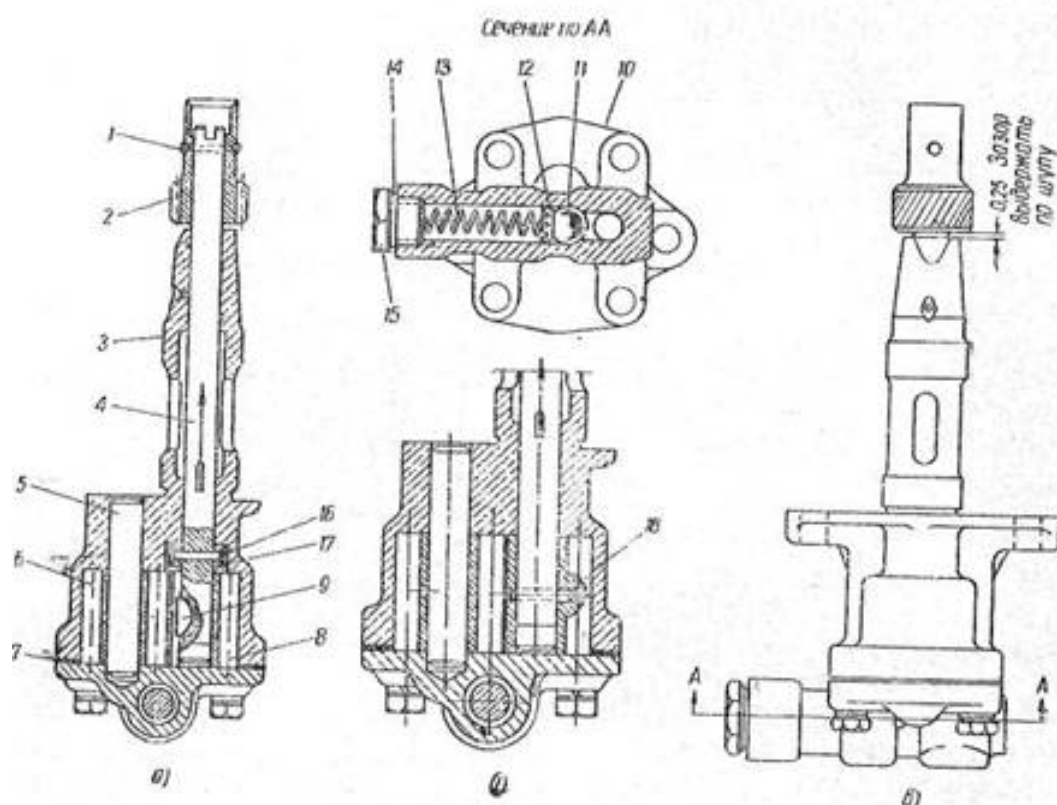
Масляный насос двигателей ГАЗ-51 и ЗИМ-12:
